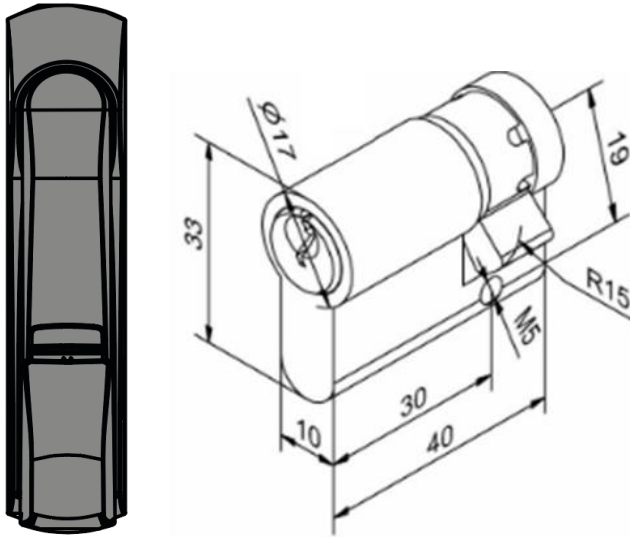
Schwenkhebelverschluss und Schließzylinder (Abmessungen in mm)
